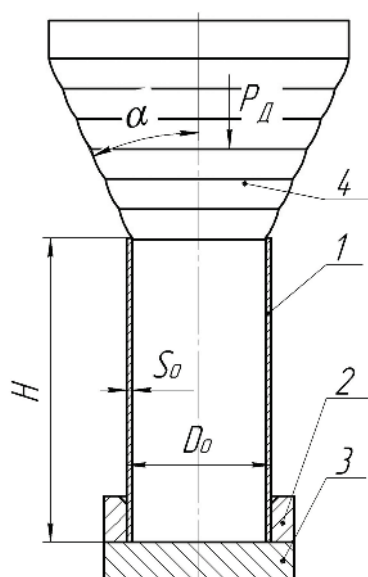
Схема процесу відкритої роздачі трубчастої заготовки
